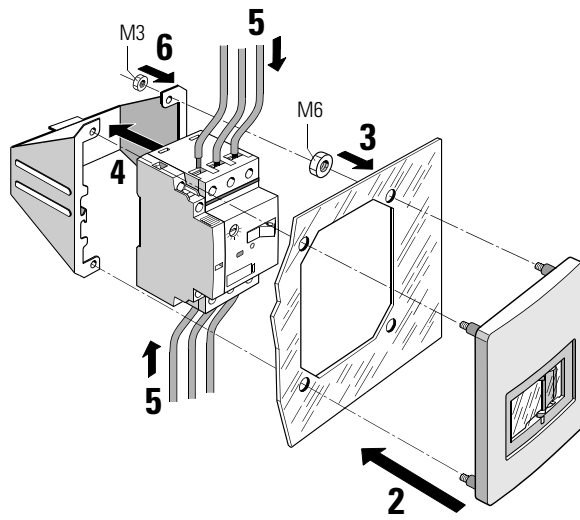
Frontplattenmontage (Beispiel: Baugröße S00)
